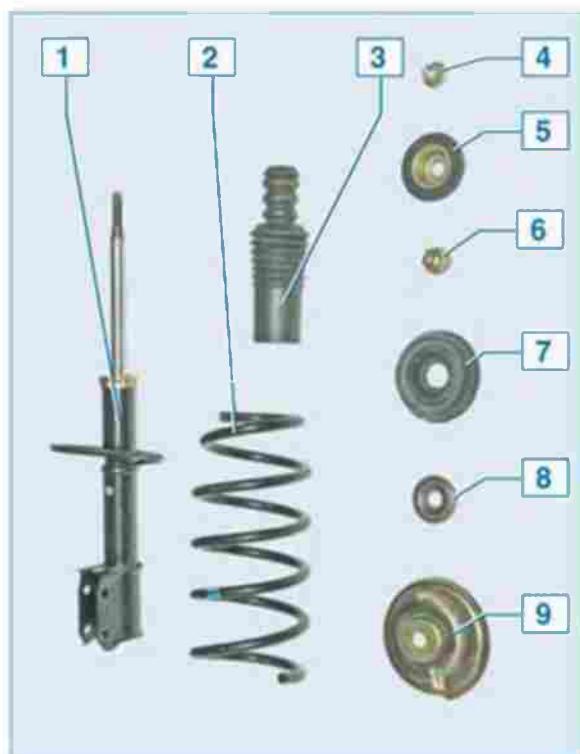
Детали амортизаторной стойки: 1 - телескопическая стойка; 2 - пружина; 3 - буфер хода сжатия с защитным чехлом; 4 - гайка крепления стойки к кузову; 5 - опорная шайба; 6 - гайка крепления верхней опоры; 7 - верхняя опора стойки; 8 - подшипник верхней опоры; 9 - верхняя чашка пружины.
